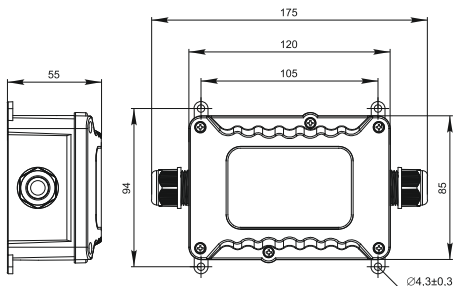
Габаритные размеры коробки WTP-409 / Figure 9 – Overall dimensions of the WTP-409 box
